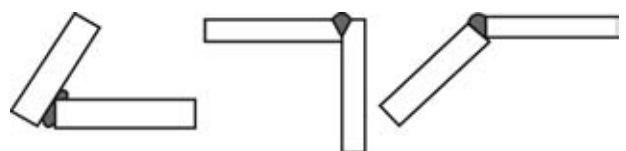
Варианты типовых соединений при изготовлении переходников для высоконагруженных сварных конструкций из разнородных материалов [3]
